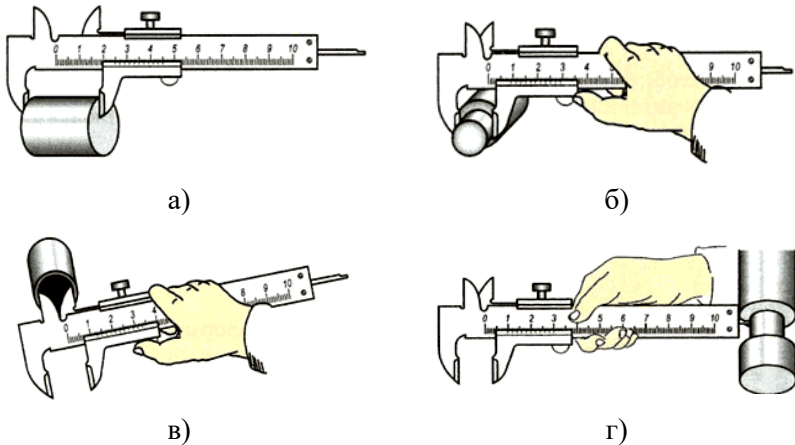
Вимірювання і контроль розмірів деталей штангенциркулем:
